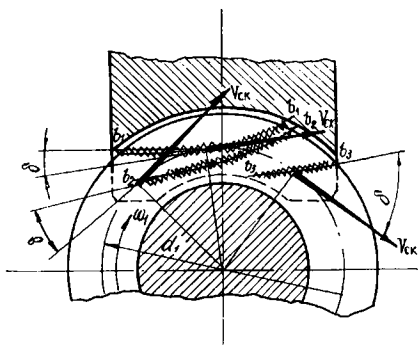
Положение контактных линий на зубе колеса червячной цилиндрической передачи.
